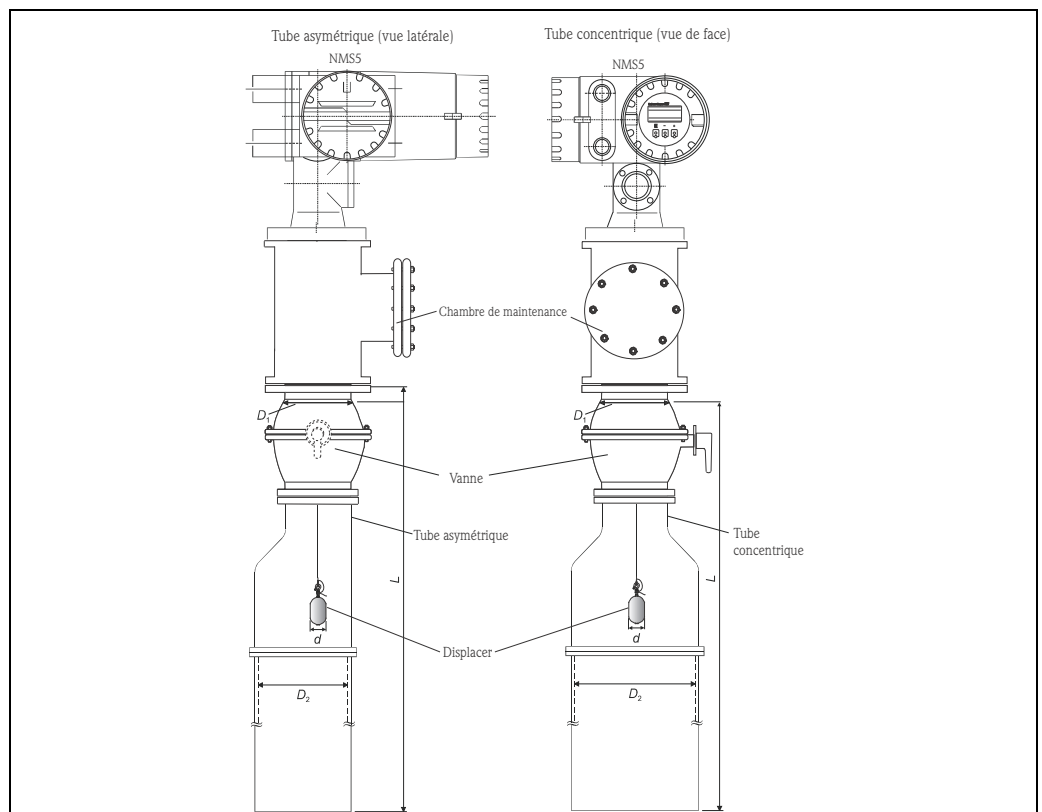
Montage dans un tube de mesure : tube asymétrique et tube concentrique
